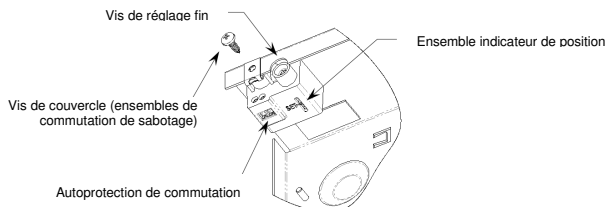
Position d'assemblage d'autoprotection 'coquille' en ceinture de style
